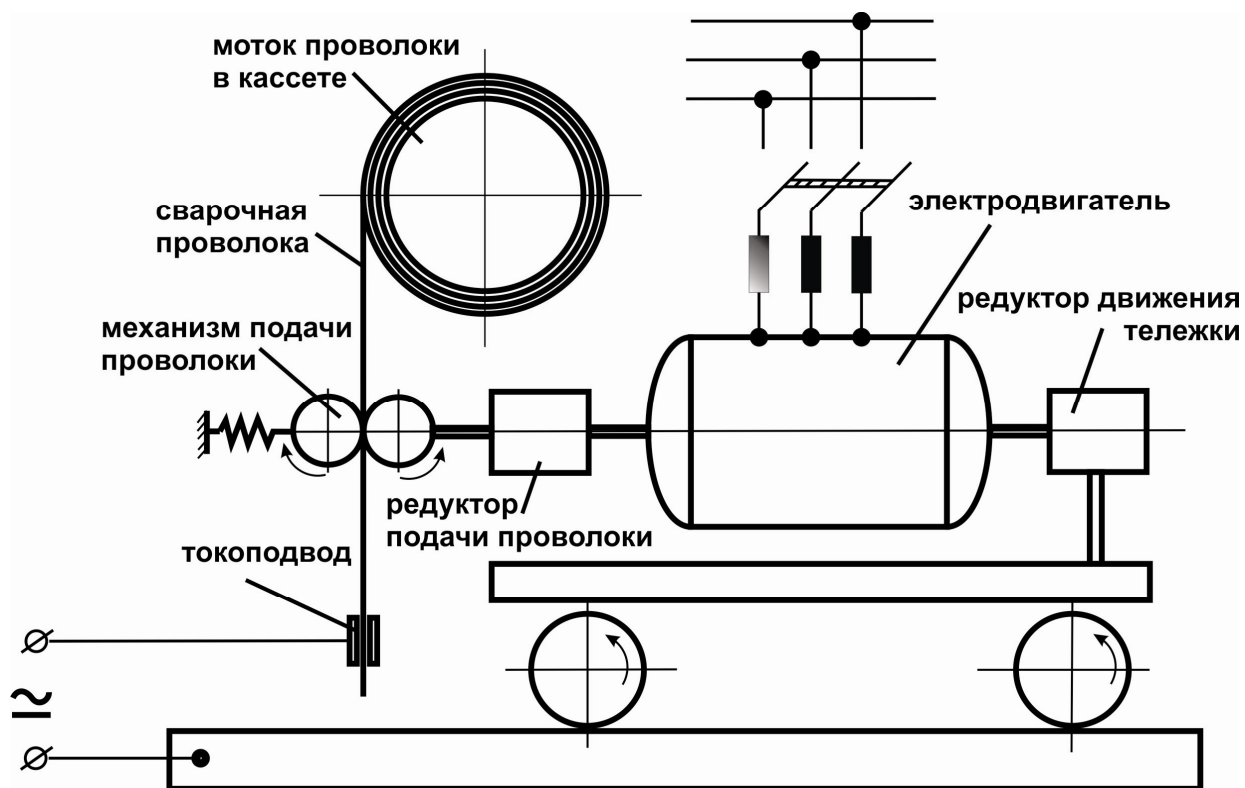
Кинематическая схема автомата для сварки под флюсом
